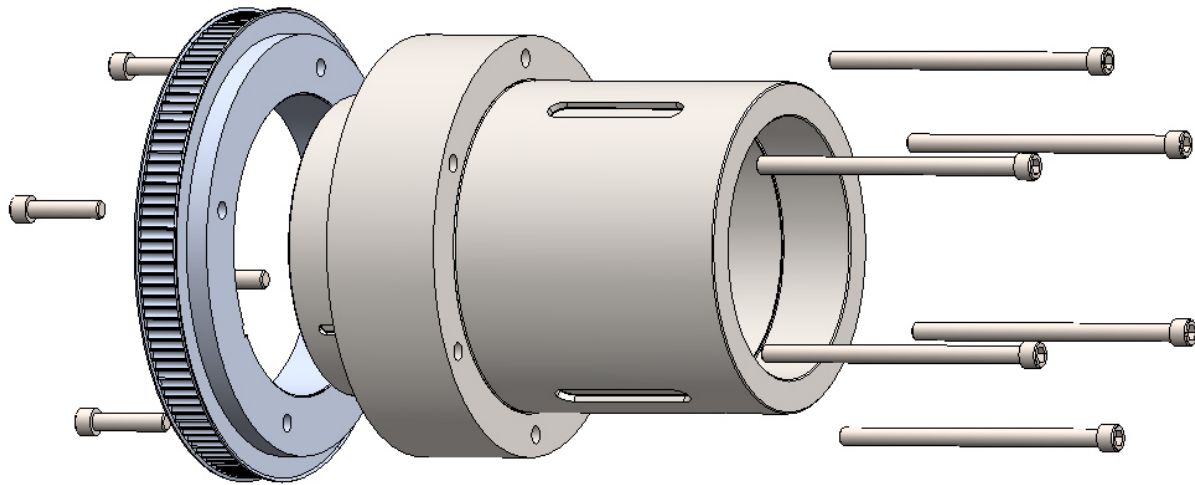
Vista explosionada de conjunto fijo. Fuente: Original
